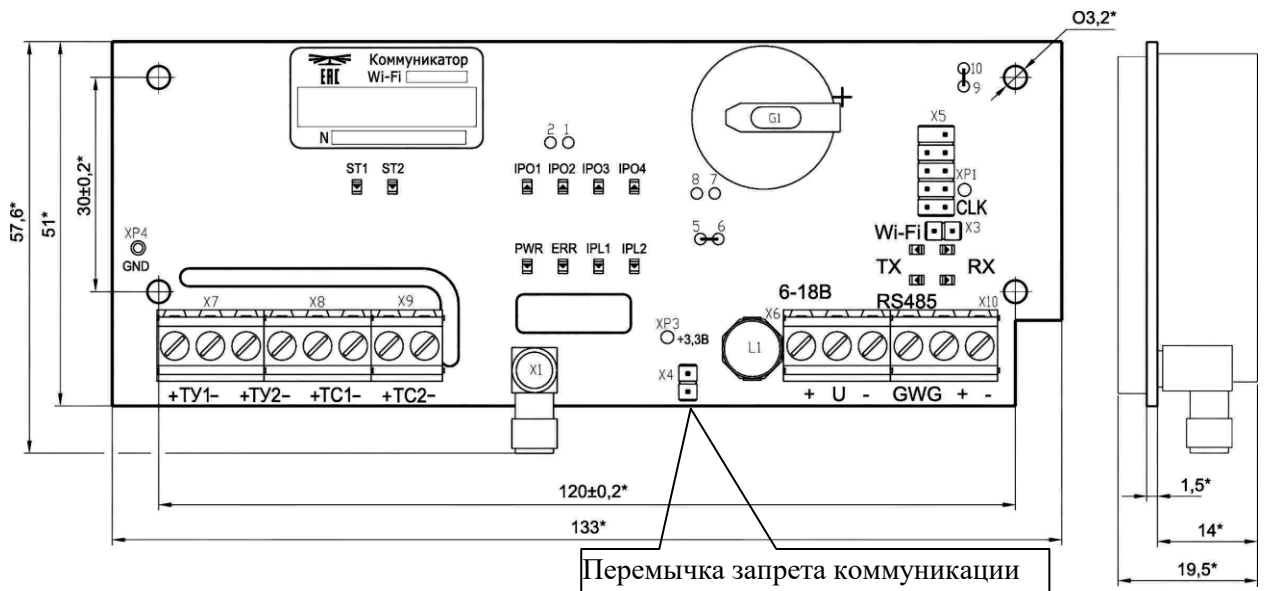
Габаритный чертеж и установочные размеры коммуникатора Wi-Fi TE102.01.01
